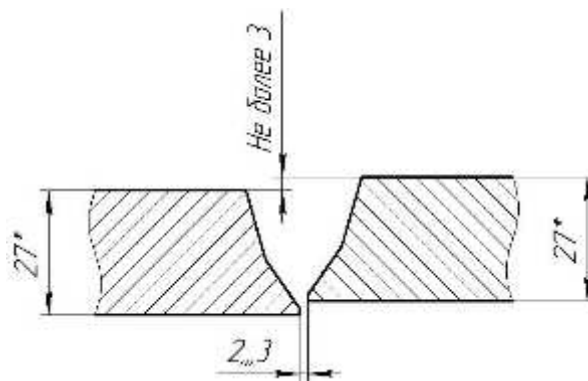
Общий вид стыка, подготовленного под сварку
